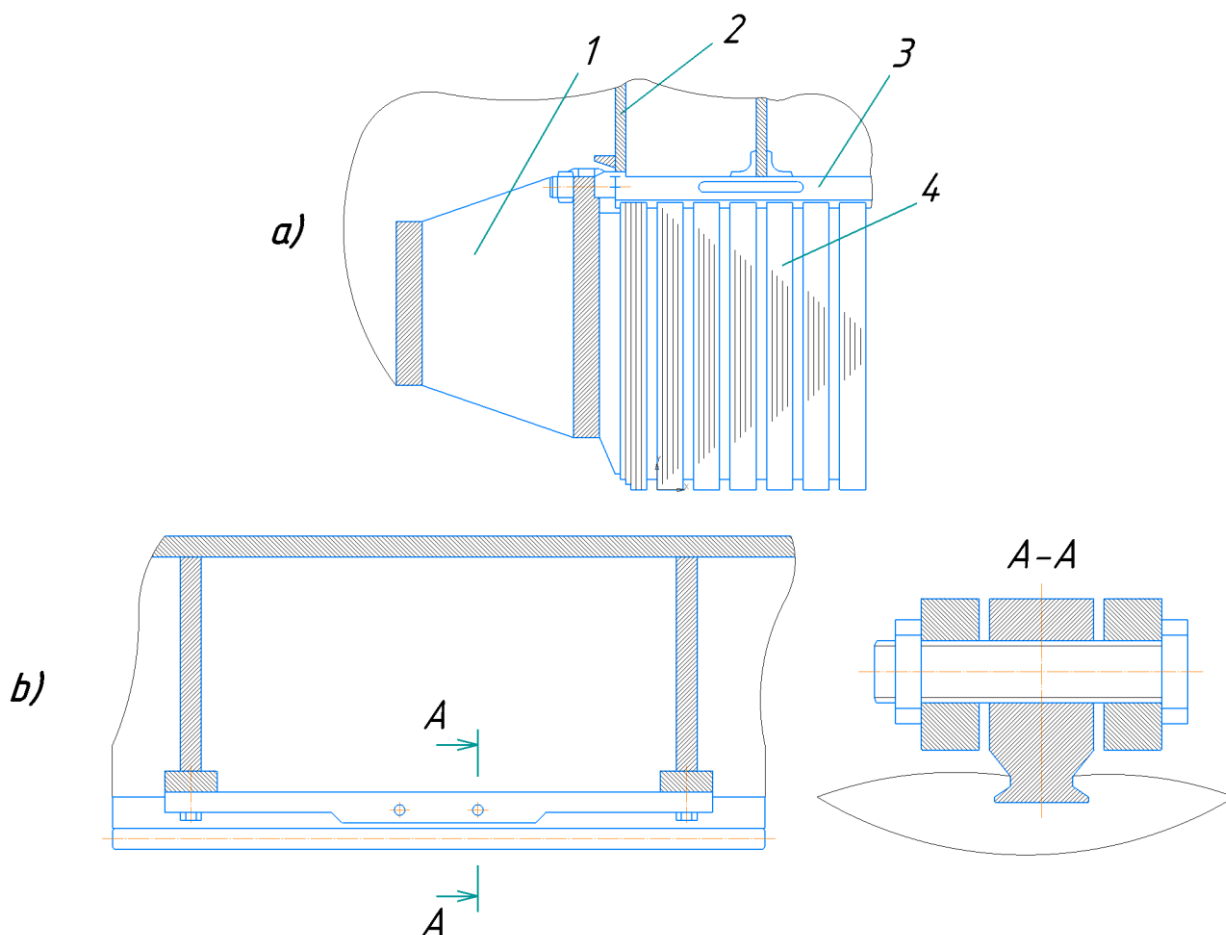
Еластична і пружна підвіска осердя в корпусі статора (1 – натискний фланець; 2 – корпус статора; 3 – призма; 4 – активна сталь)
